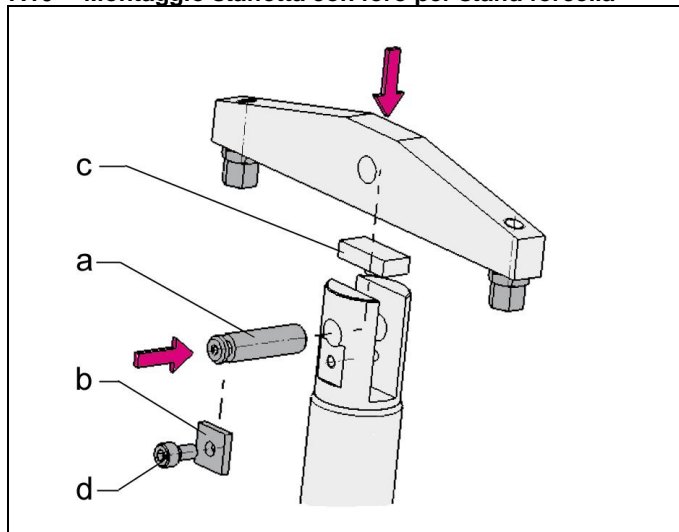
Montaggio / smontaggio della staffetta oscillante
